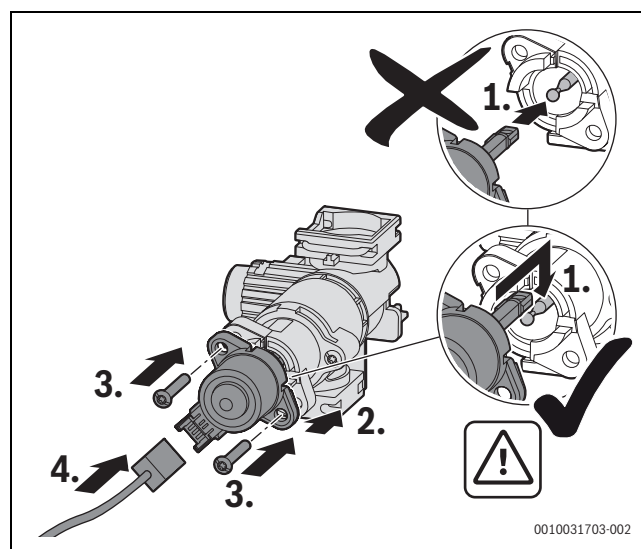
Remonter le moteur au niveau de la vanne sélective (variante avec vis)
